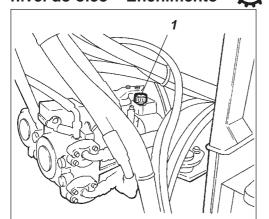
Engrenagem da bomba 1. Vareta do nível
